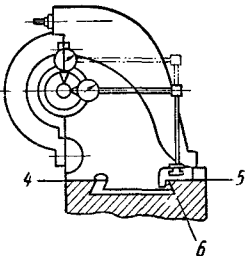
Проверка точности кинематической цепи зубострогального станка.
